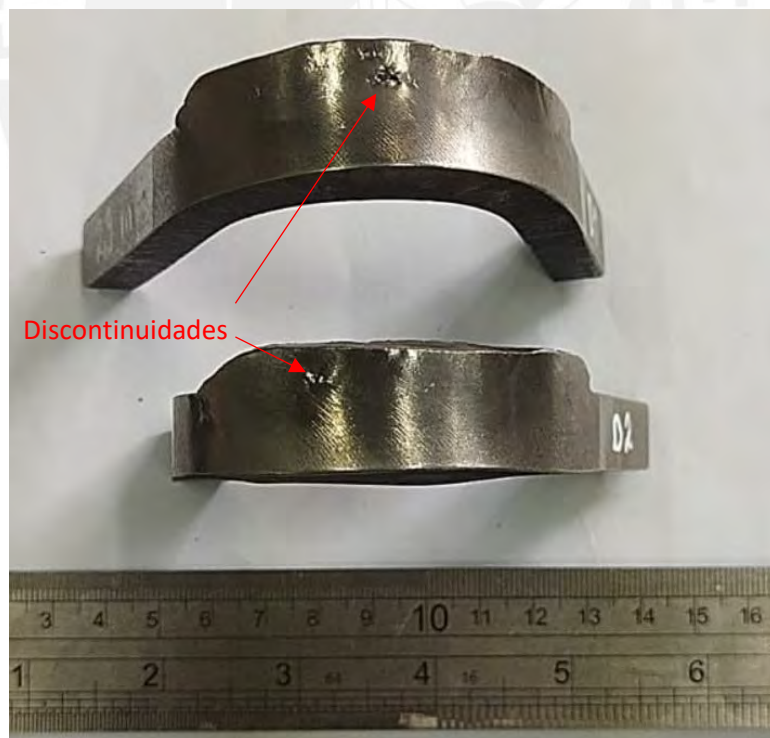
Cupones de soldadura sometidos a ensayo de doblado.
